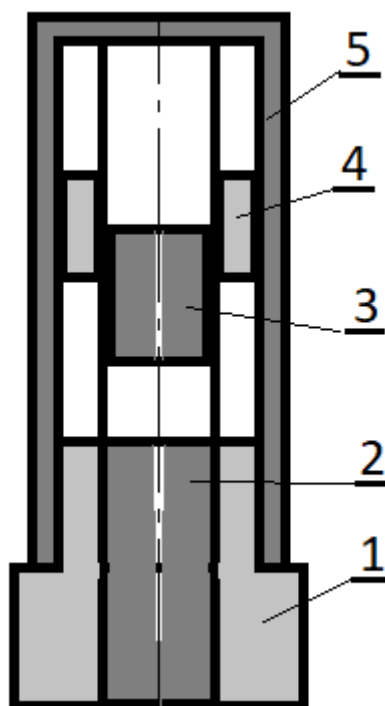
Подвійний занурний пневмоударник: 1- зовнішній буровий інструмент; 2 – внутрішній буровий інструмент; 3 – внутрішній поршень; 4 – зовнішній поршень; 5 – корпус
